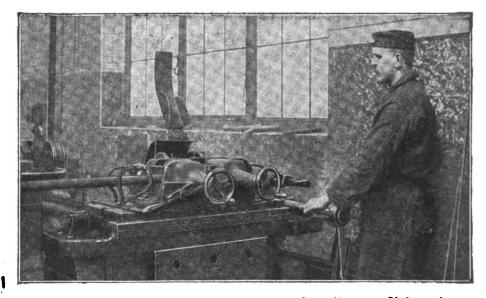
Elektrische Schweißmaschine für das Schweißen von Siede- und Rauchrohren in der Eisenbahnhauptwerkstatt Nied.
